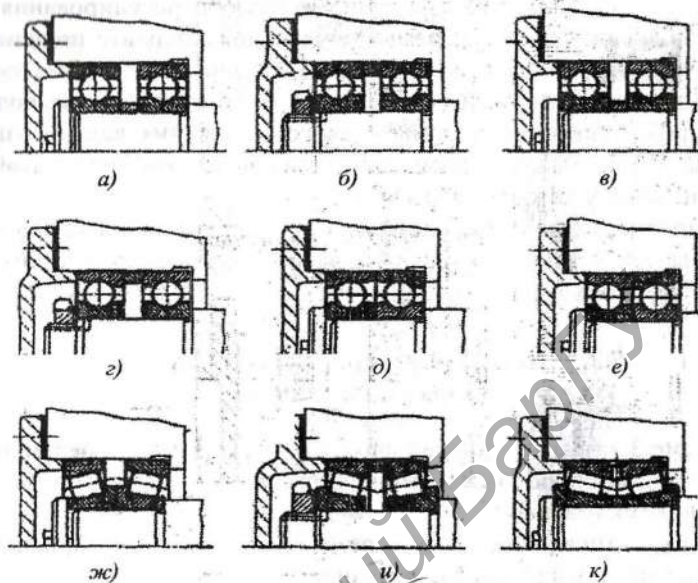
Фиксирующая опора с двумя подшипниками [9, с. 112]
